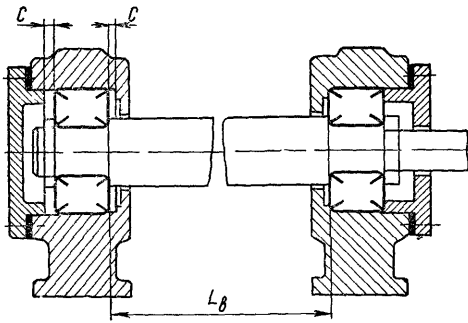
Схема установки подшипников — фиксирующая и плавающая опоры
